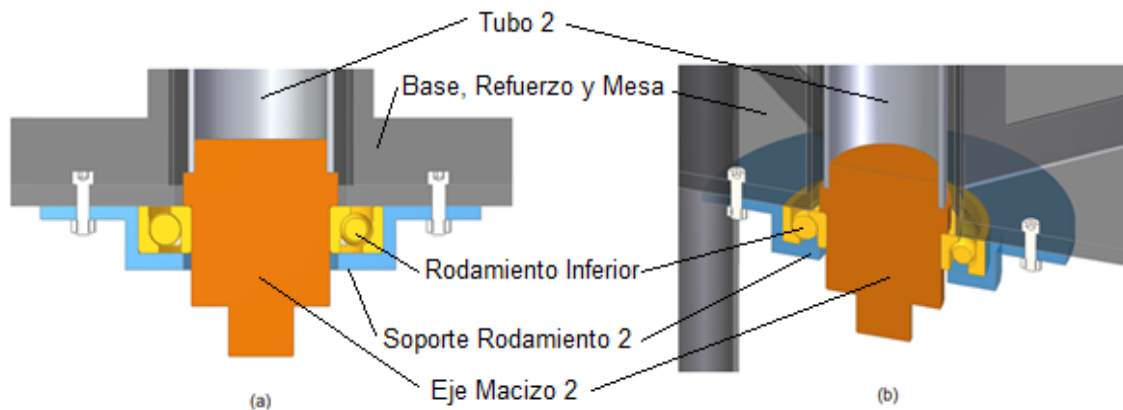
Acople para el segundo rodamiento de alineación del subsistema eje con soporte anclado por tornillos al refuerzo. (a) Vista en corte frontal. (b) Vista en corte isométrica.
